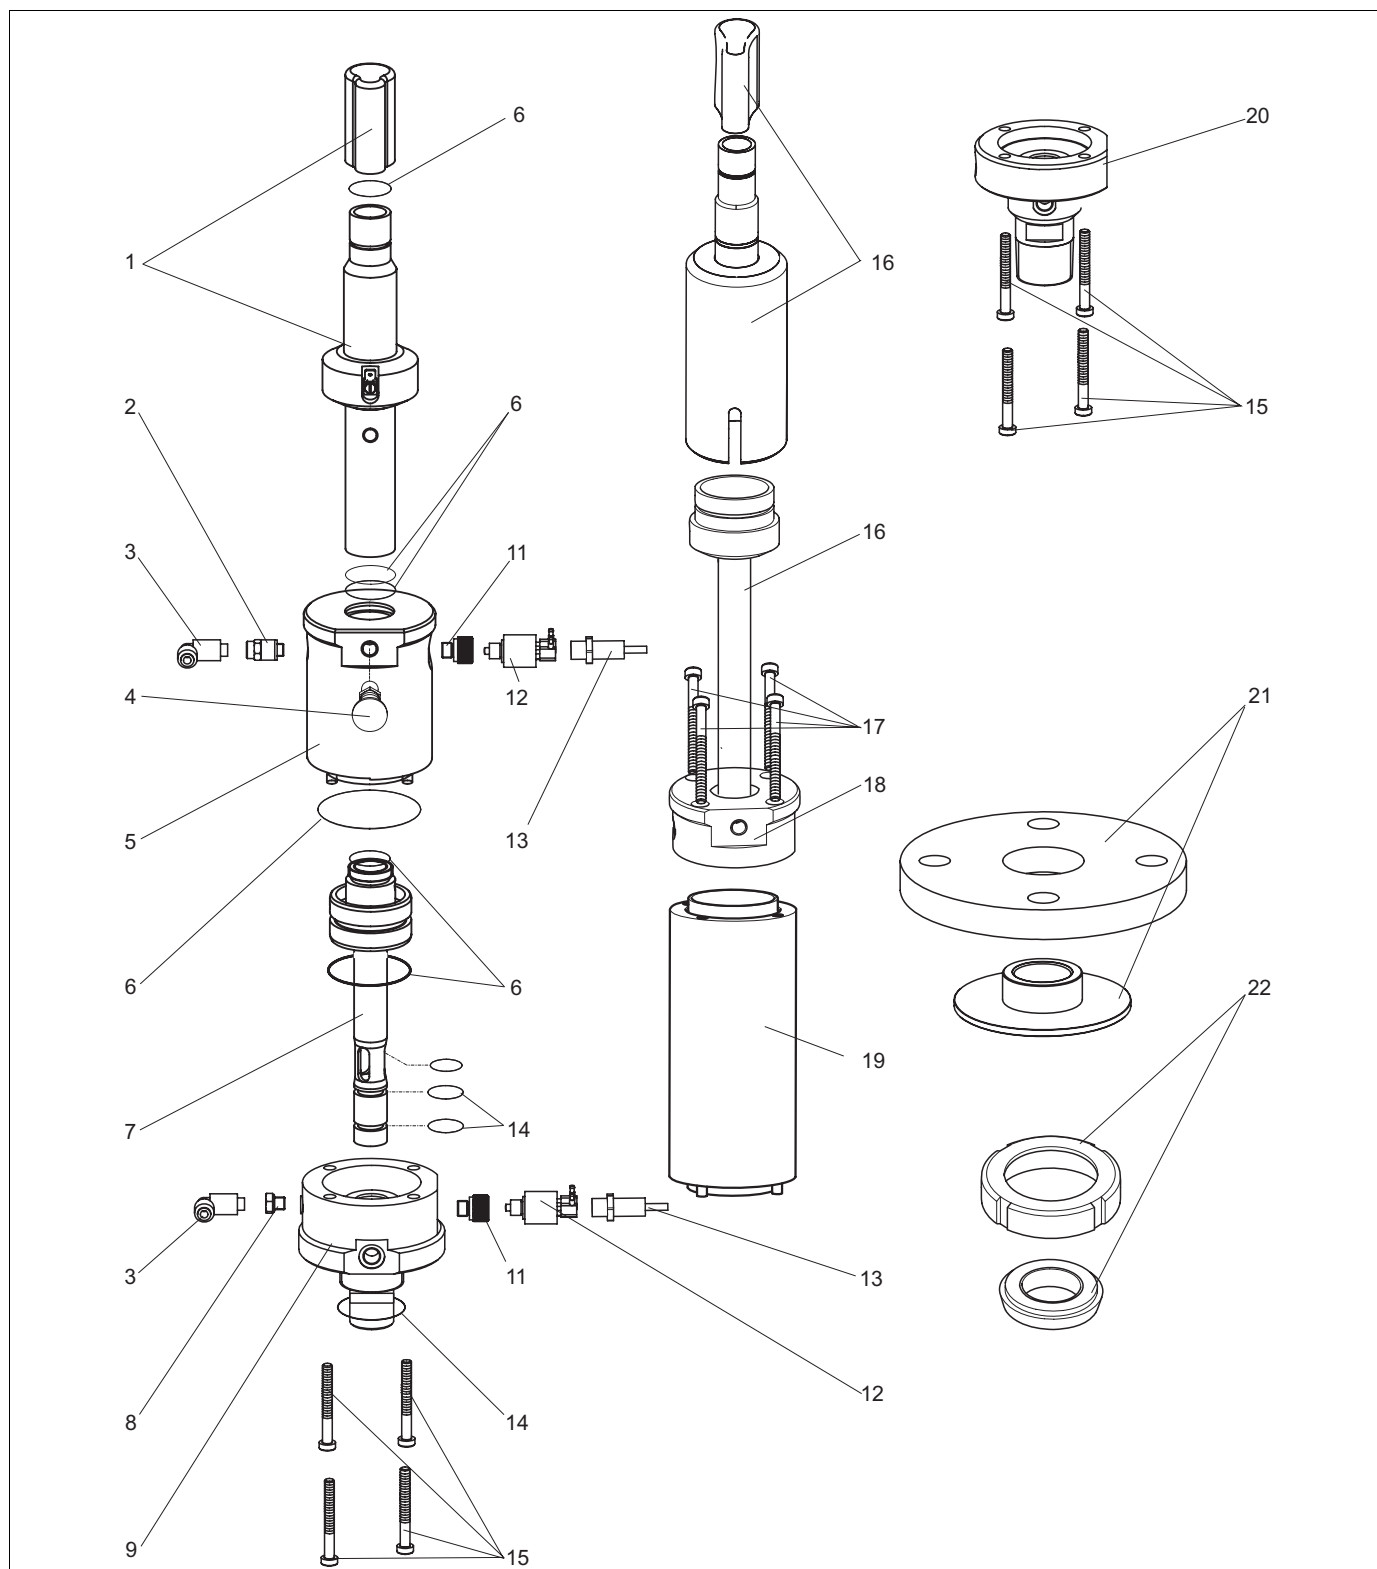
Parti di ricambio (per tutte le versioni dell'armatura)
